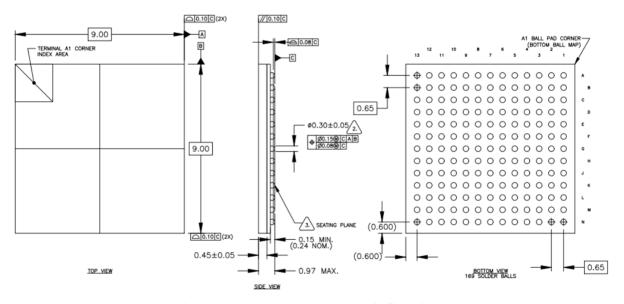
MH1903 BGA1699mm×9mm 封装尺寸
